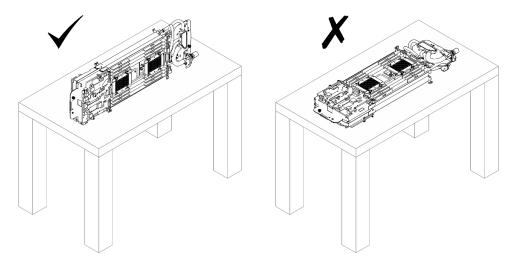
Handhabung des Wasserkreislaufs vor der Installation im Einbaurahmen
